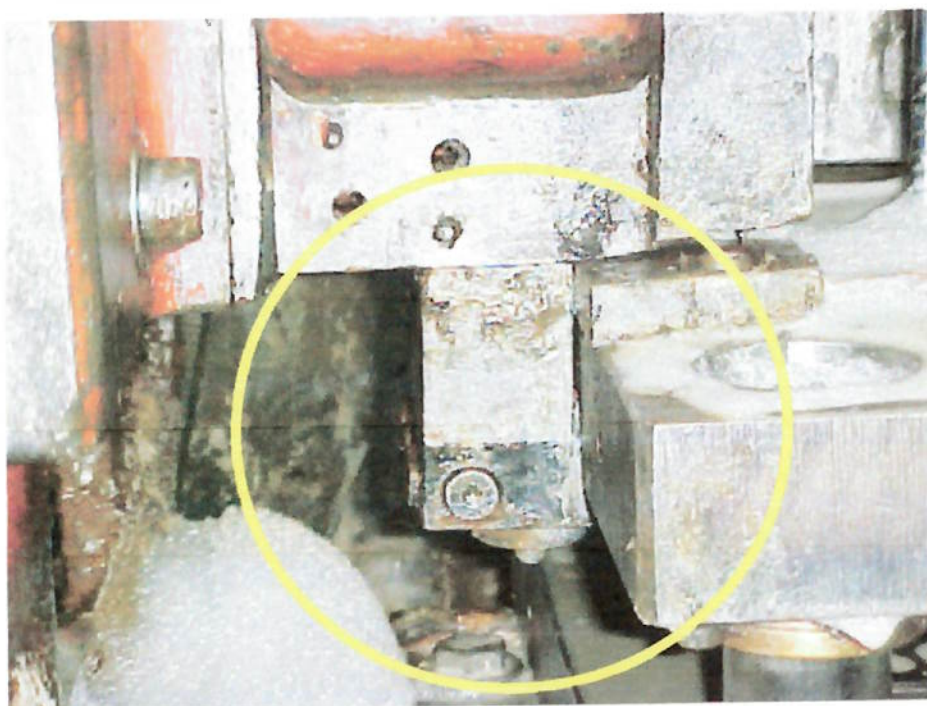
Dispositivo hidráulico para fixação do bloco (base superior)
